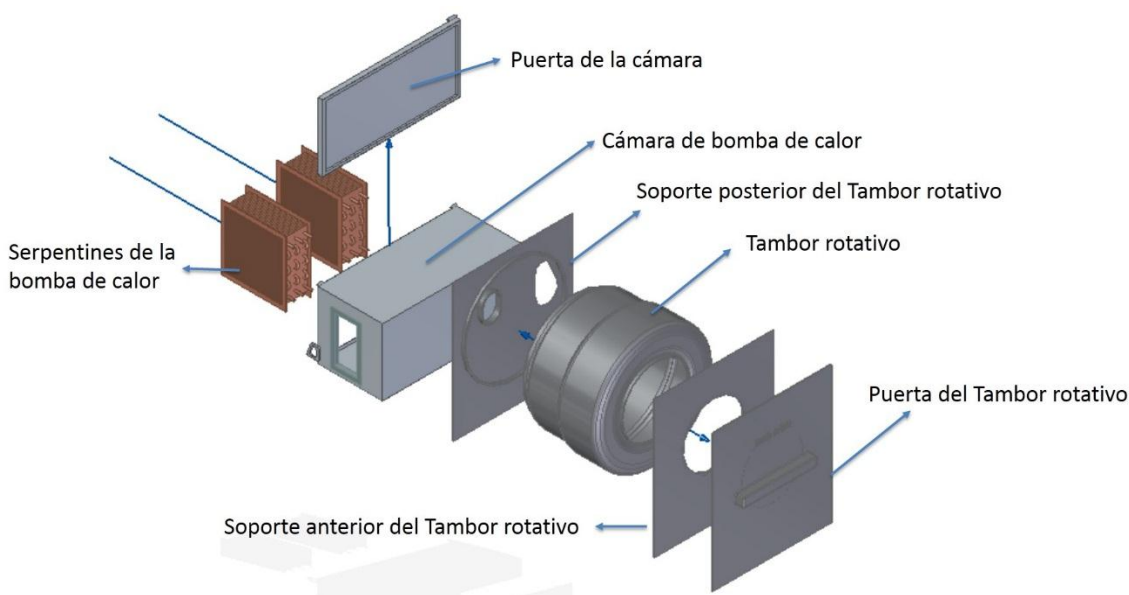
Ensamble de los subsistemas, montaje real fuente: autor
